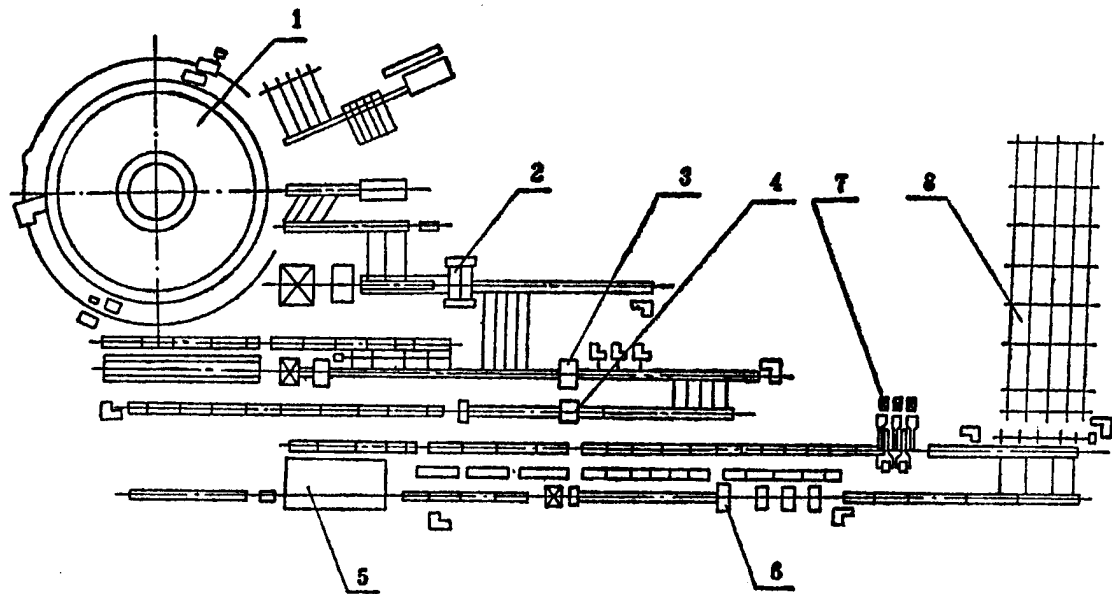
苏联第一乌拉尔新钢管厂三辊轧管机组平面布置图
